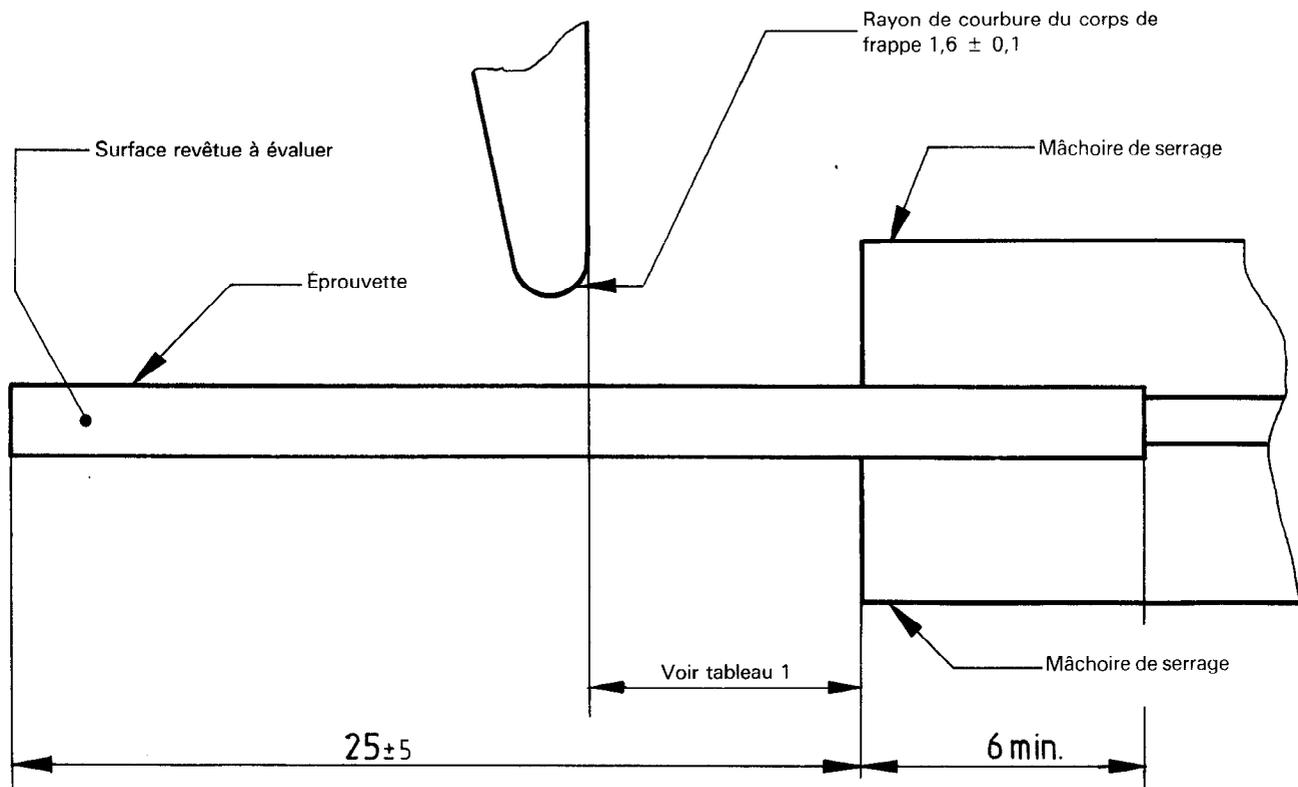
Mâchoires de serrage de l'éprouvette et corps de frappe
